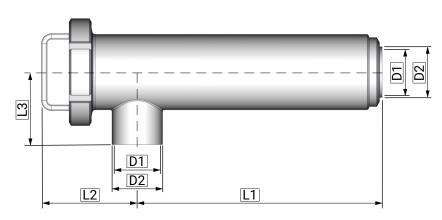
Beispielzeichnung mit Schweißanschluss
